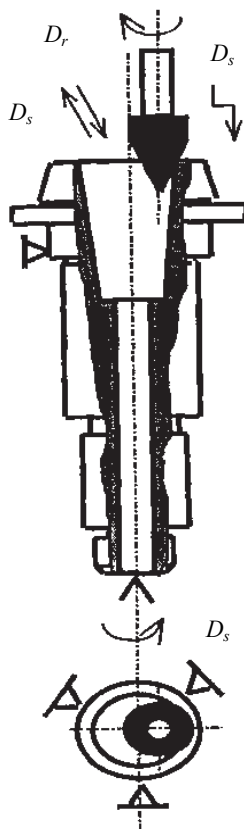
Схема обработки базовой фаски на центрошлифовальном станке
